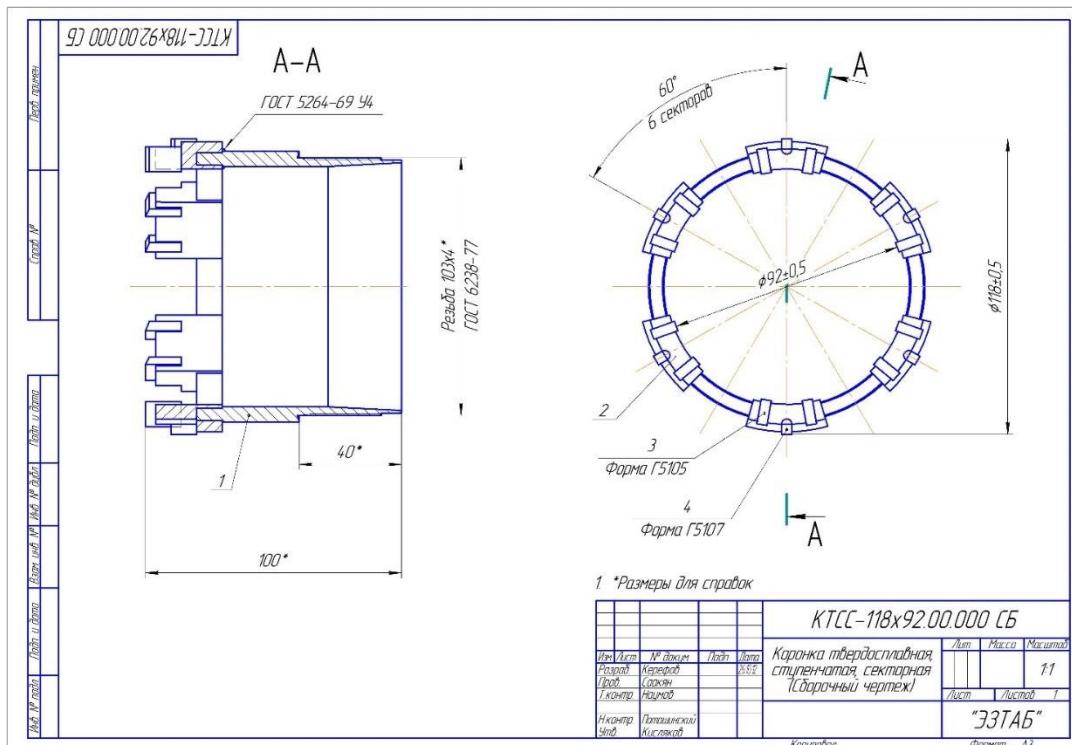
Чертеж твердосплавной секторной ступенчатой коронки
